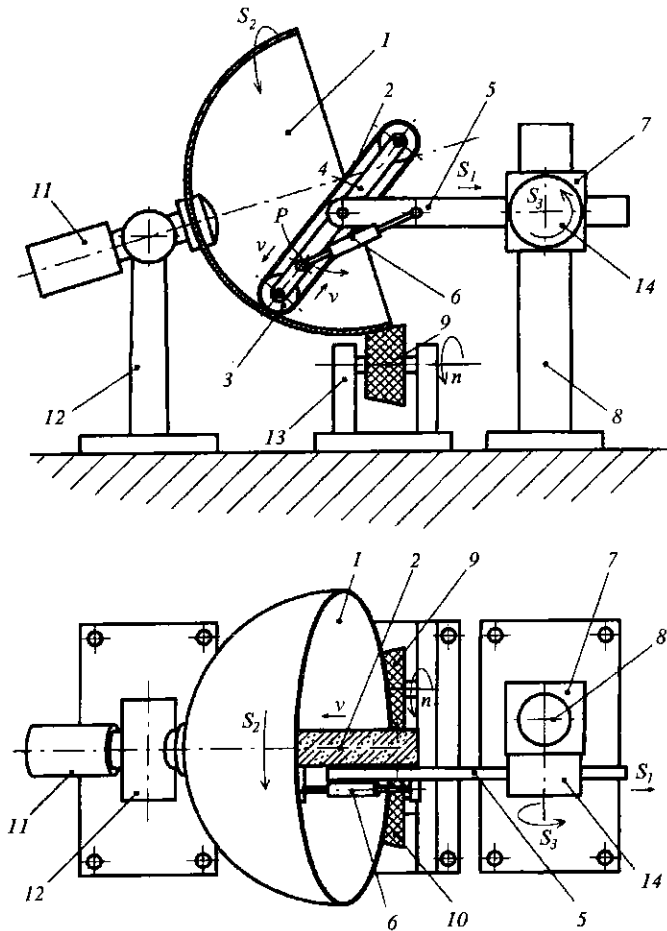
Схема ленточного шлифования крупногабаритных деталей сложной конфигурации: 1 — деталь; 2 — абразивная лента; 3 — прижимной ролик; 4 — рычаг натяжения ленты; 5 — траверса; 6 — гидроцилиндр; 7 — коробка скоростей; 8 — колонна; 9 — ведущий ролик; 10 — опорный ролик; 11 — электродвигатель; 12 — стойка; 13 — опора; 14 — поворотный механизм;  $n$  — частота вращения ведущего ролика;  $S_1, S_2, S_3$  — движения подачи;  $P$  — сила прижима абразивной ленты к обрабатываемой поверхности;  $v$  — скорость главного движения
